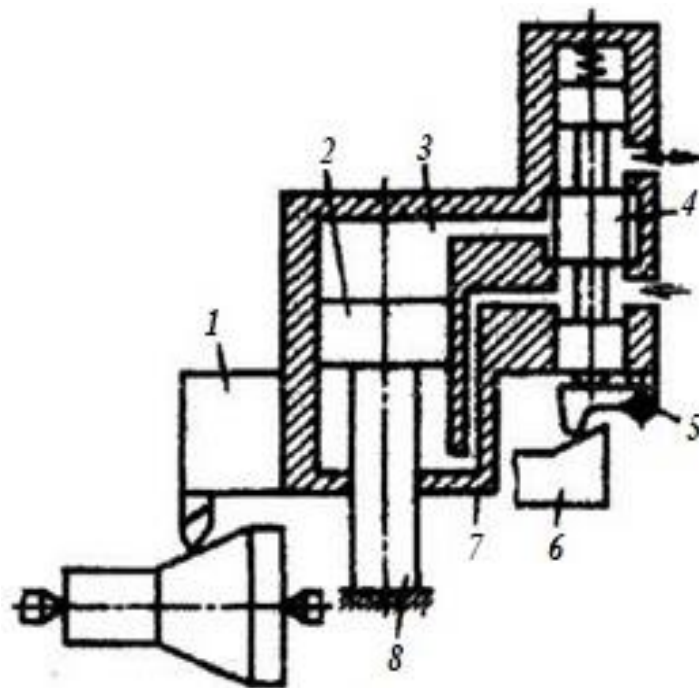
Слідкуючий гідропривод копірувального верстата
